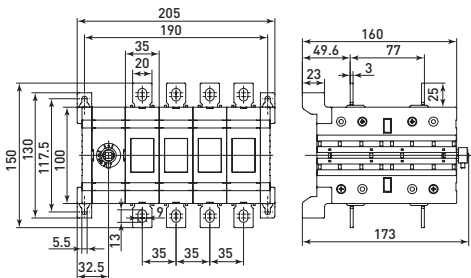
Габаритные и установочные размеры реверсивных рубильников 160-250А 4Р
